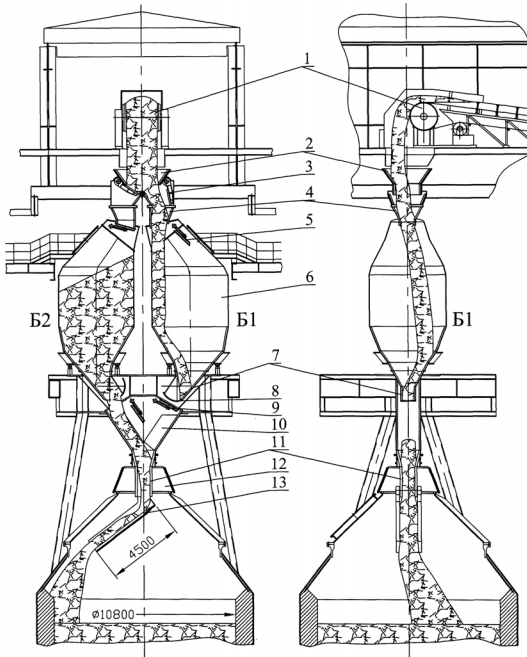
Общий вид бесконусного загрузочного устройства ДП №9.
